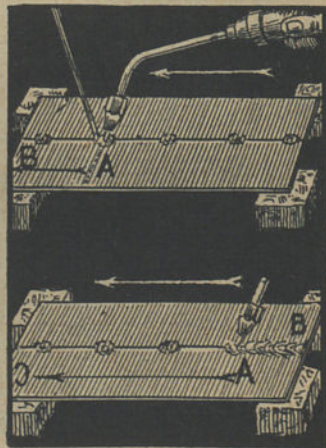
Sentido em que se executam as soldaduras.
